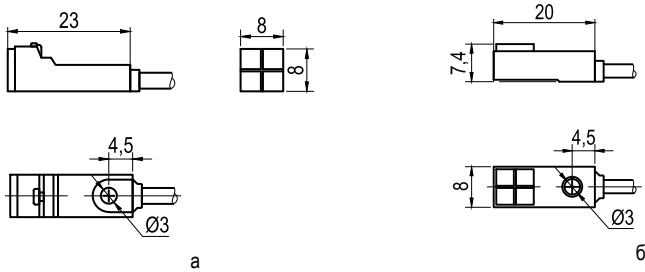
Габаритные и установочные размеры датчиков с шириной корпуса 8 мм
